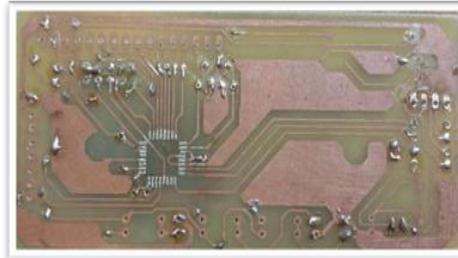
Alur PCB Mikrokontroler Atmega328p
